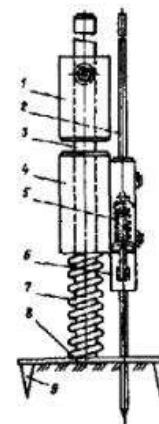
Приспособление для забивки заземлителей, опираемое на землю:
